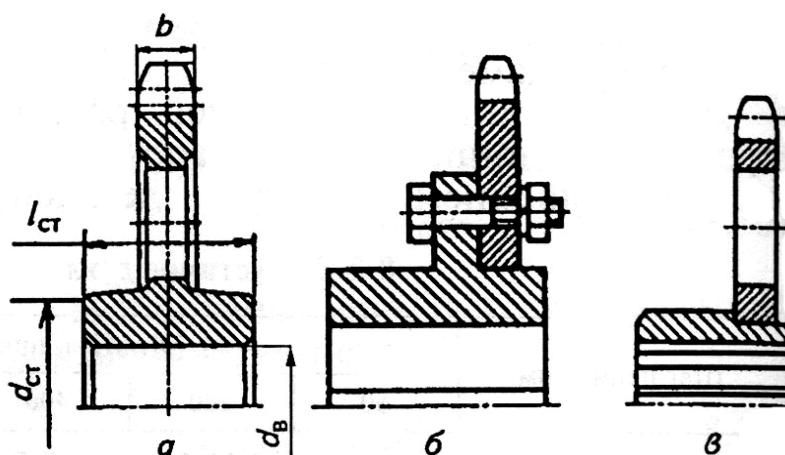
Звездочки цепной передачи: *a* – цельная; *б* – составная; *в* – сварная
